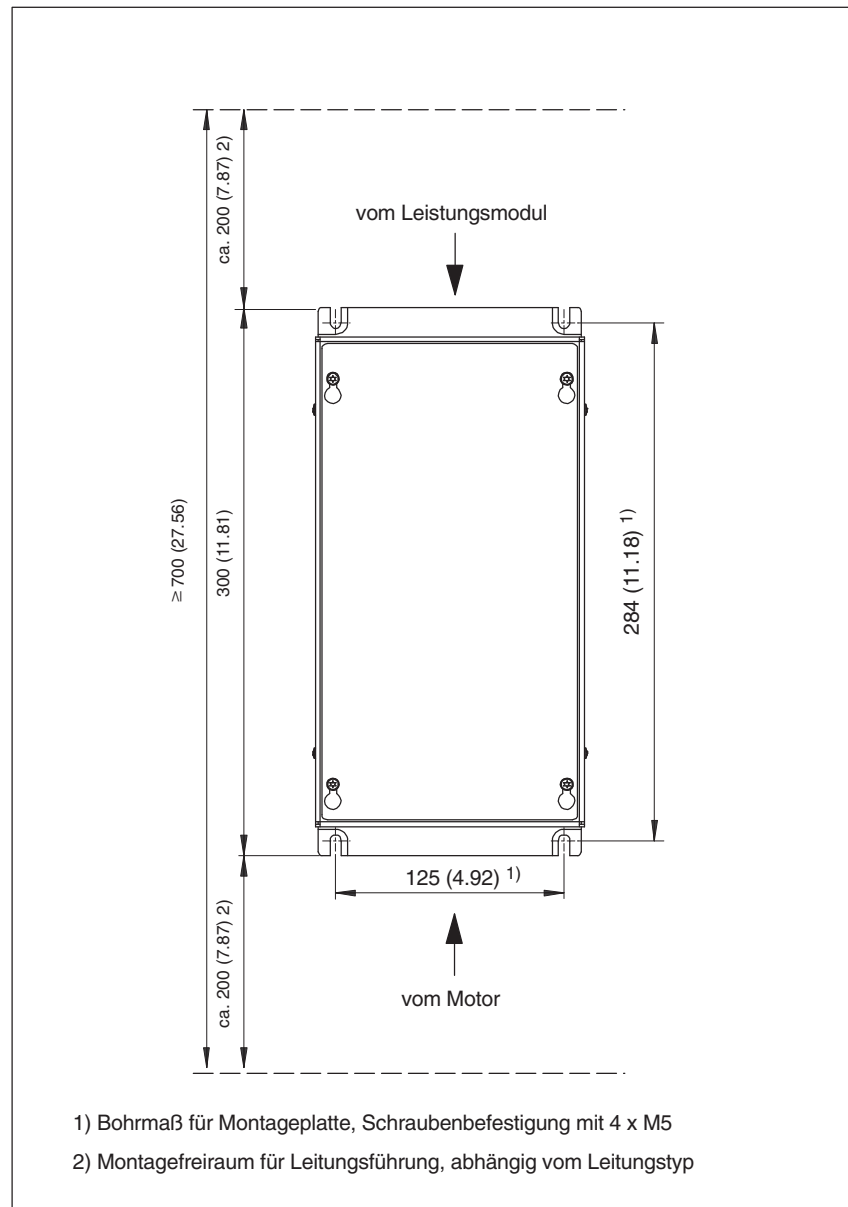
Montagemaße für ein Voltage Protection Module VPM120
